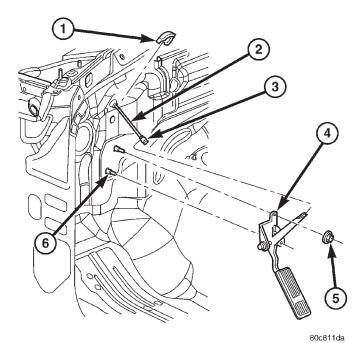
CONJUNTO DE PEDAL DEL ACELERADOR Y SOPORTE
